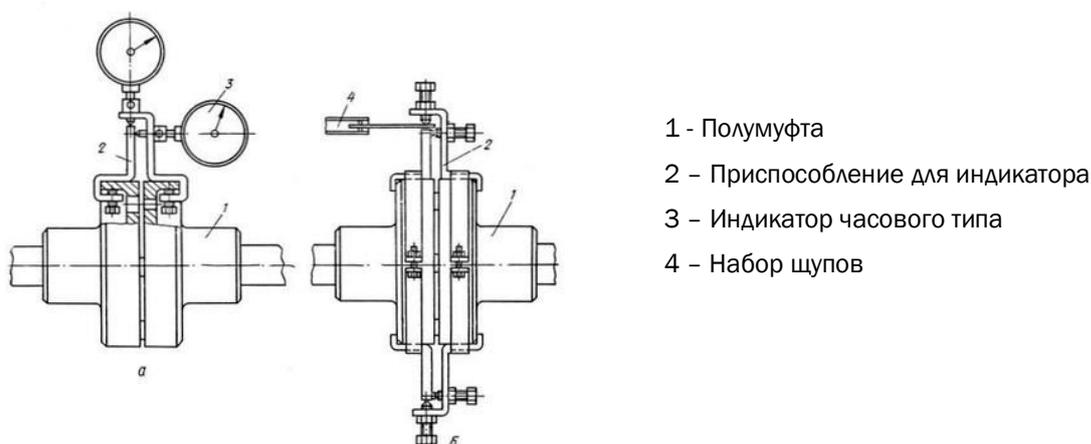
Приспособления для контроля центровки по полумуфтам:
